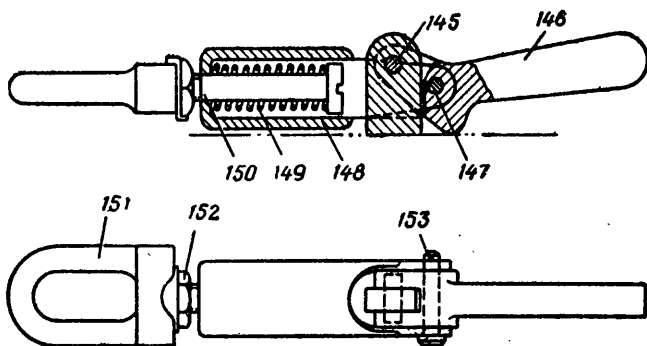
Приспособление старой конструкции для крепления по-походному опорной плиты (Сб14-2):
